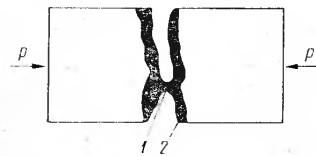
Оплавление свариваемых поверхностей при стыковой сварке:
